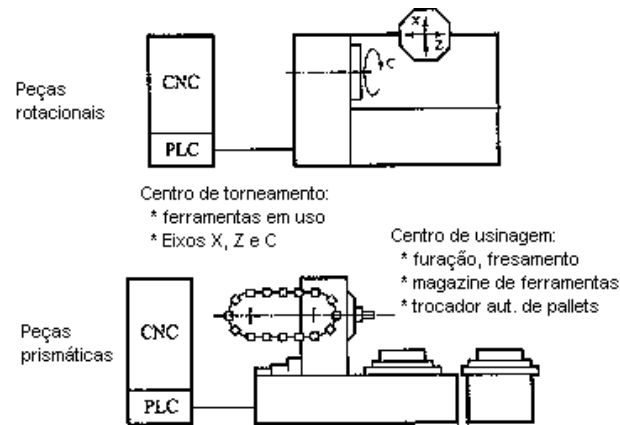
Centros de usinagem, os elementos básicos de uma célula flexível de manufatura
